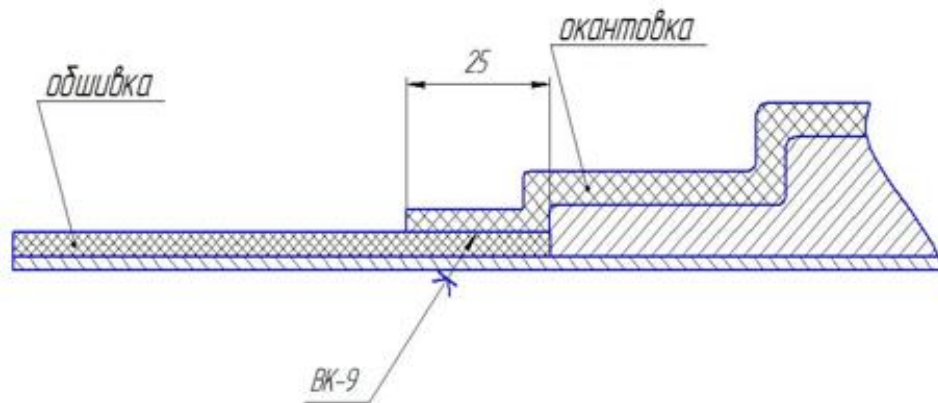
Схема склейки обшивки з окантовками люкового отвору з використанням епоксидного клею ВК-9
